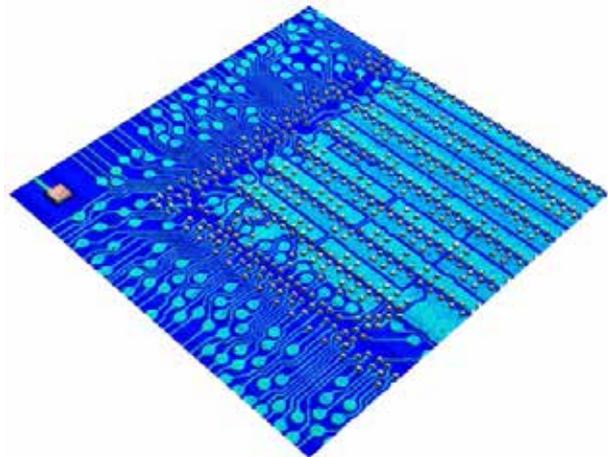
3D-Messung einer Platine mit Bump-Kontakten.
